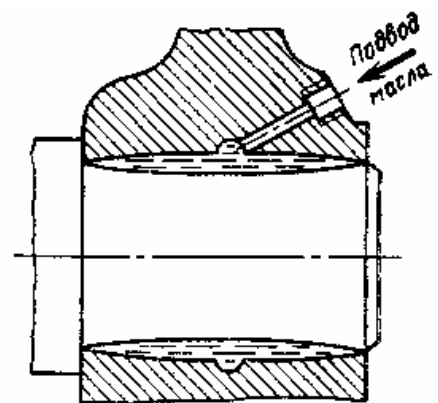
Поддача масла при разборке соединений гидропрессовым образом
